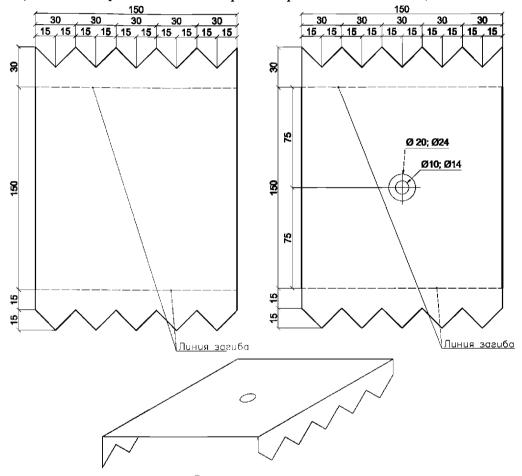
Анкер НЕОПОРМ® для скрытого крепления теплоизоляции на кровле
